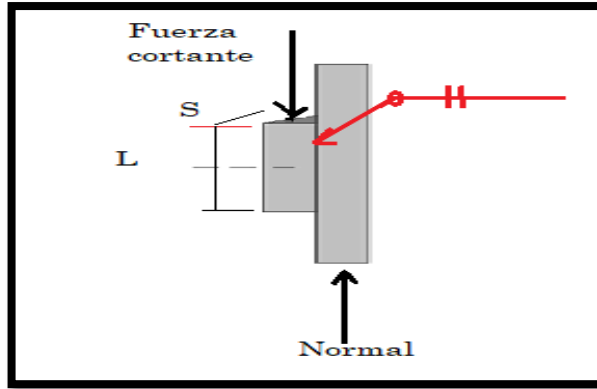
D. C. L. Para soldaduras sometidas a fuerzas de corte
